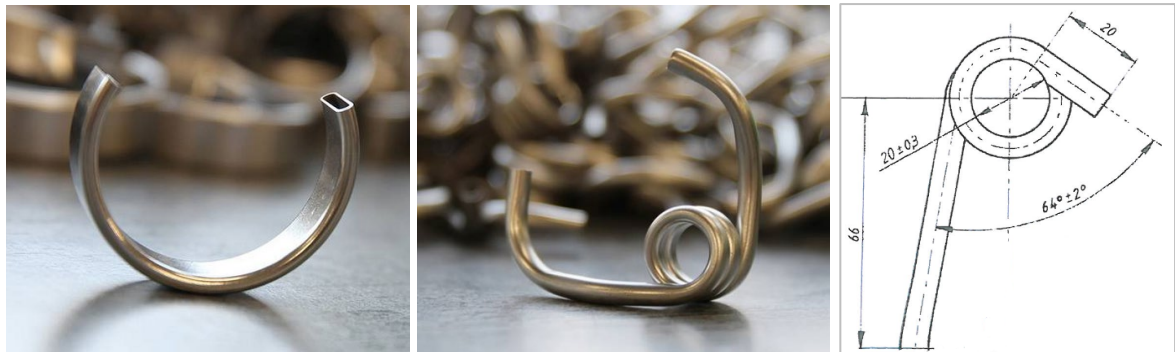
Bourdon-Kreisfedern (Links) sind für Drücke bis ca. 60 bar und Bourdon-Spiralfedern (Mitte) sind für Drücke bis ca. 4'000 bar erhältlich. Die Zeichnung (Rechts) zeigt die Dimensionen der vermessenen Spiralfedern (NG160, Rohrdurchmesser 7 mm). (Quelle: BK Feinmechanik)
